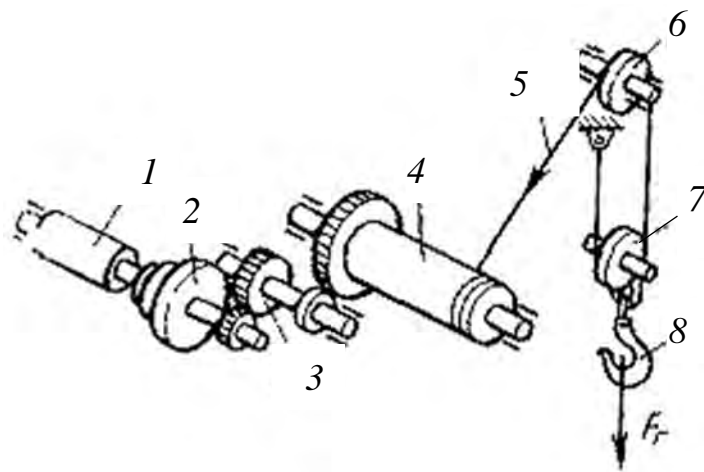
Схема механизма подъема: 1 – двигатель; 2 – тормоз; 3 – трансмиссионный механизм; 4 – барабан; 5 – гибкий элемент; 6 – отклоняющий блок; 7 – траверса (обойма); 8 – грузозахватное устройство
